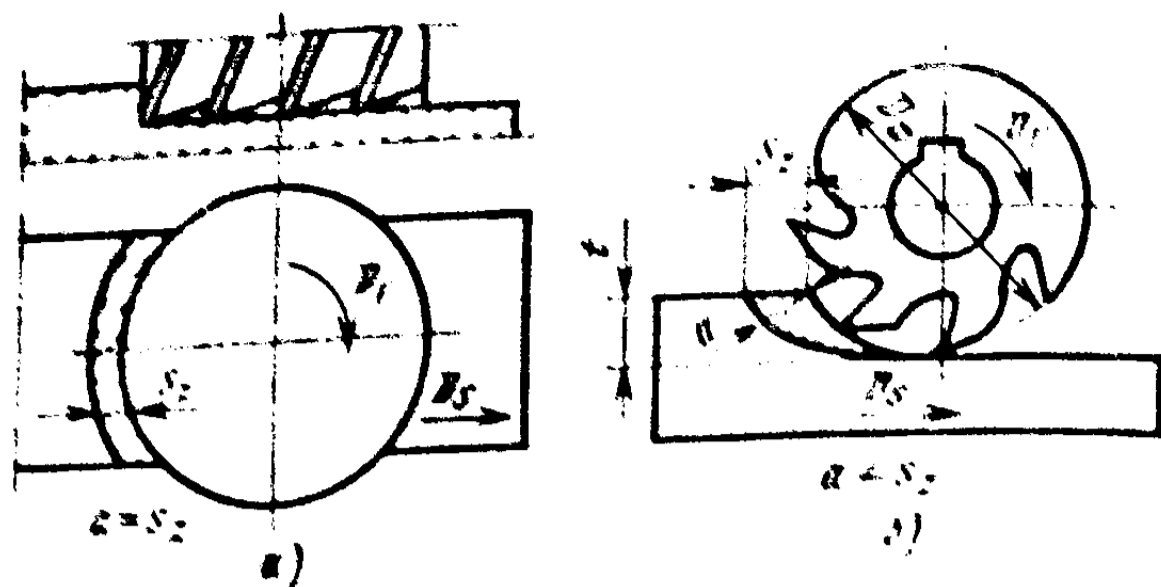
Толщина стружки при торцовом (а) и цилиндрическом (б) фрезеровании
